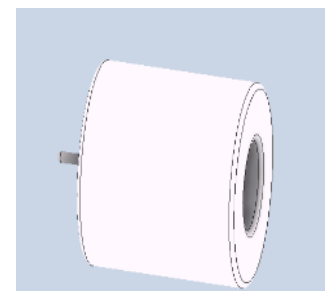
Calce del engranaje con el motor diseñado en Inventor [5].
